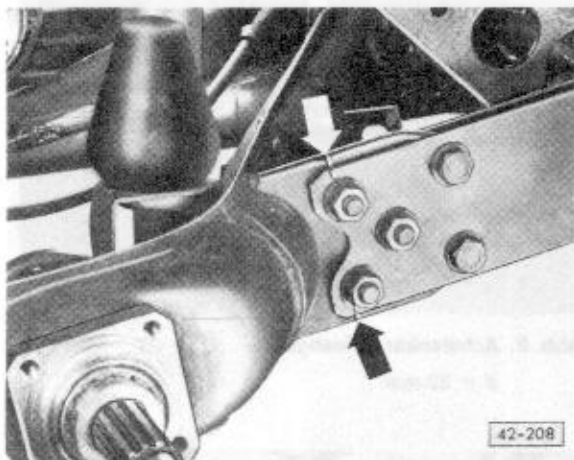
Einbaulage Federstrebe/Achsenkerflansch markieren
